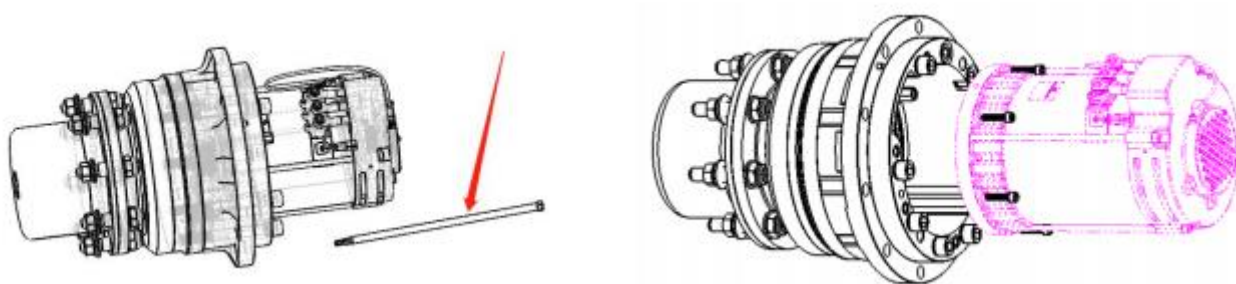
Ferramenta de desmontagem - Figura 3.2.8 Desmontagem da porca de fixação do motor de tração
